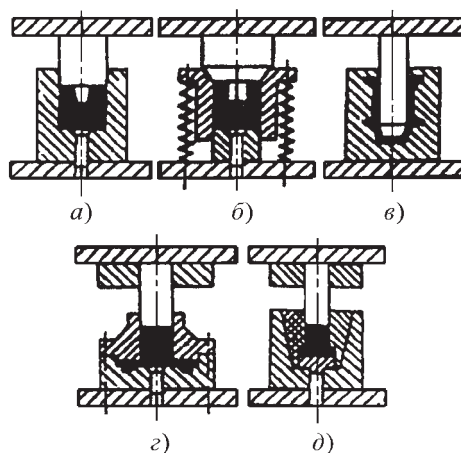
Схемы матриц пресс-форм для ШЖМ
